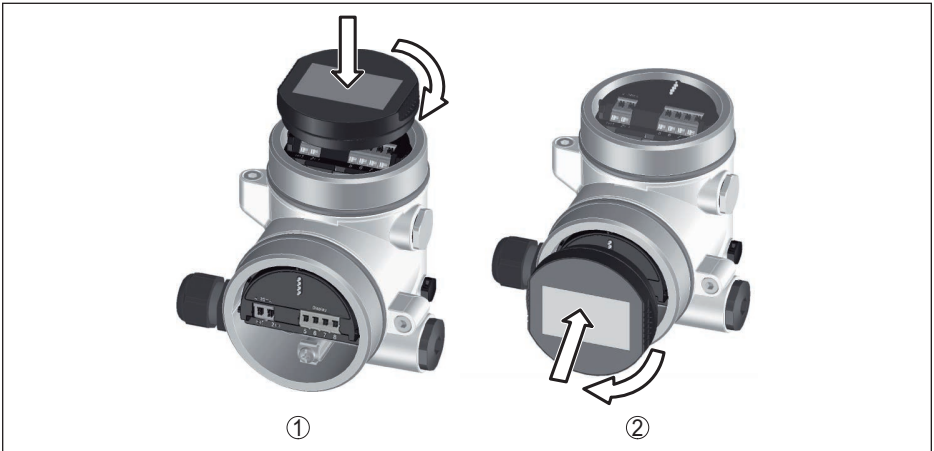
Установка модуля индикации и настройки в двухкамерном корпусе
